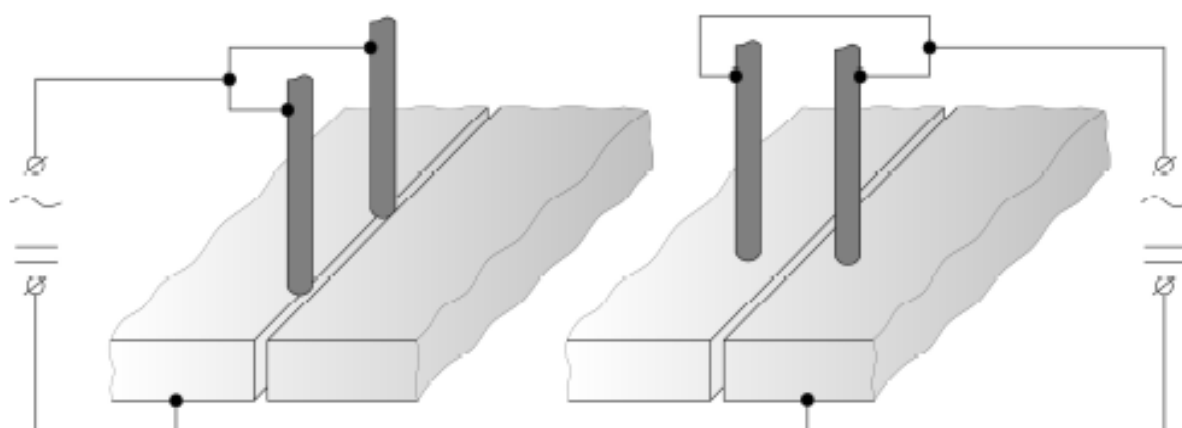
Расположение сварочных проволок при двухэлектродной сварке вдоль стыка (а) и поперёк стыка (б)
